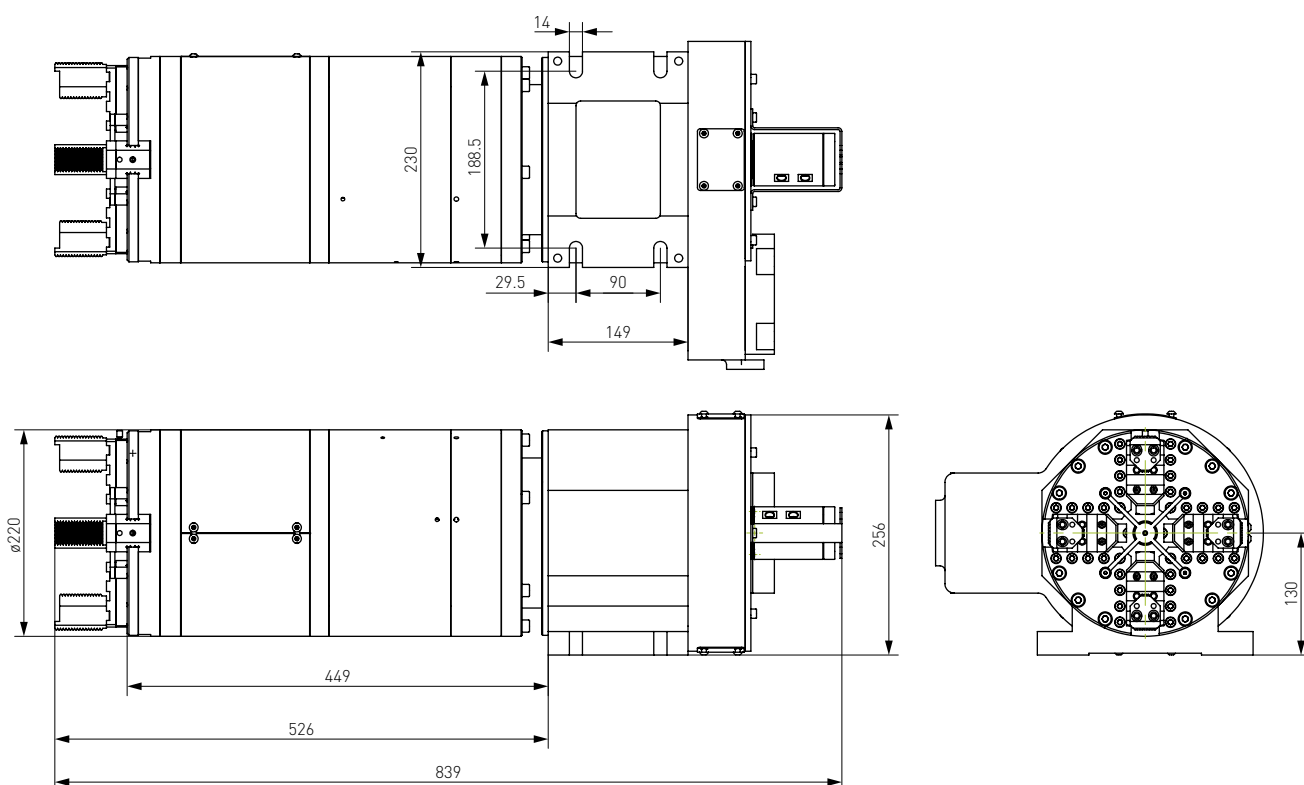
Габаритный чертеж патрона основного RKN-240E.
